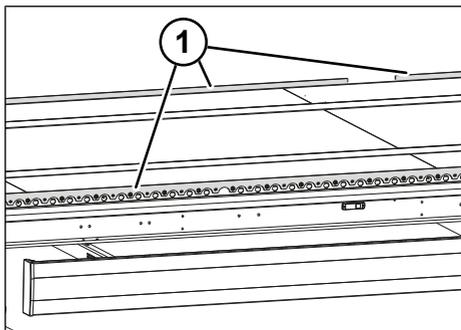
Multi Screw sul telaio esterno con foratura Multi Lock
